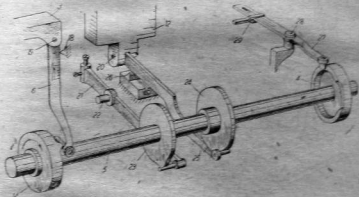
Полуавтомат Сагаф для изготовления фасонных фрез.
